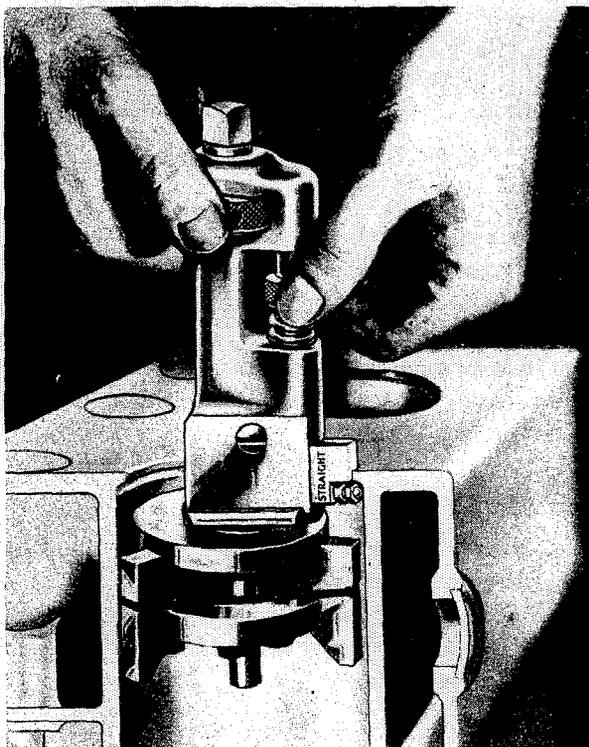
Schneidwerkzeug für Ränder in Zyl.
